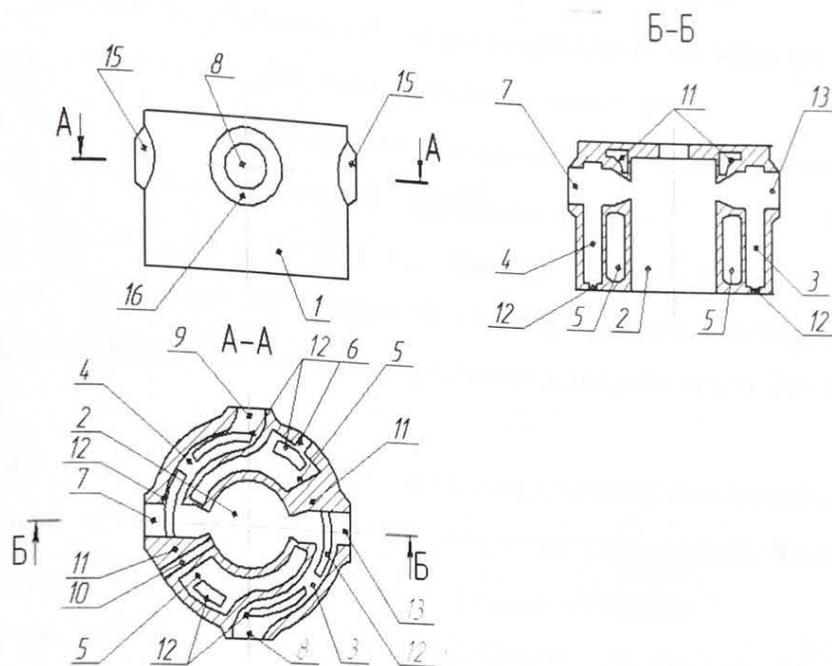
Циліндр III-ої ступені компресора удосконалений
